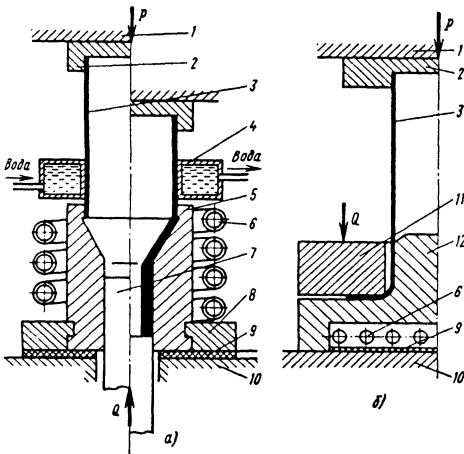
Схемы типовых штампов для обжима (а) и образования фланца (б) на трубчатой заготовке с зональным нагревом:
